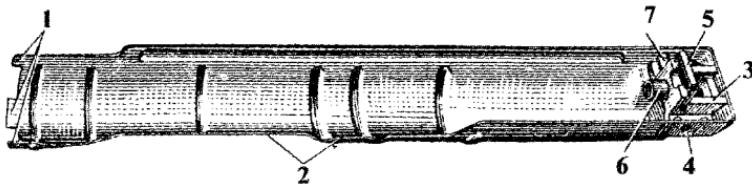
Крышка ствольной коробки СВД-63: 1 — выступы; 2 — вырезы; 3 — вкладыш; 4 — отверстие для выталкивания оси; 5 — выступ с полукруглой выемкой; 6 — цилиндрический выступ; 7 — пружинный фиксатор.
